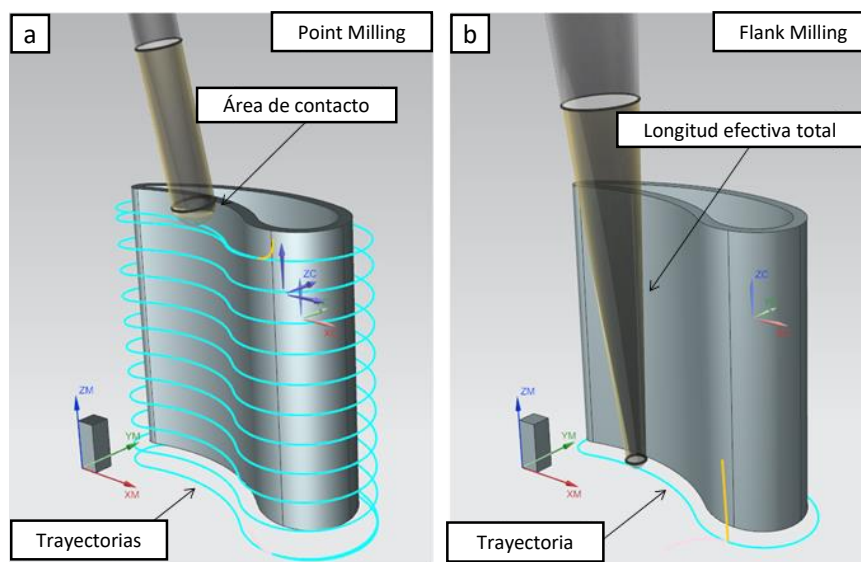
Estrategias de acabado: a) *Point milling* y b) *Flank milling*.
